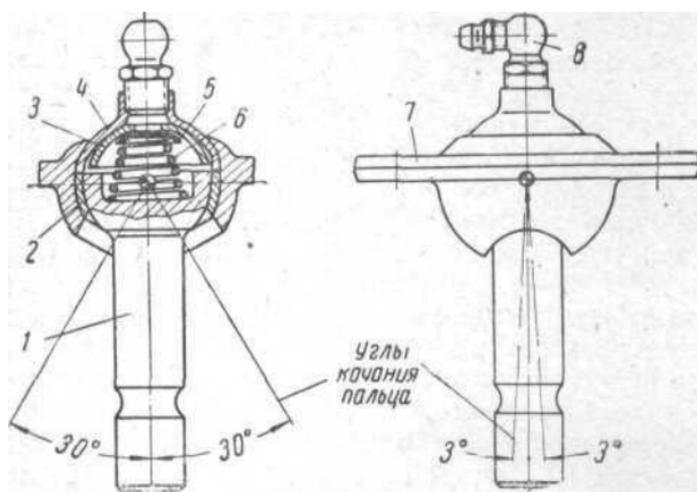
Шаровой шарнир стойки подвески автомобиля модели 407:
